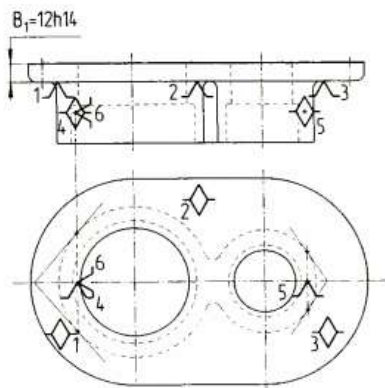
Схема базування у разі отримання чистої встановлювальної бази (поверхня 1, див. рис. 2.4) на перших етапах оброблення
